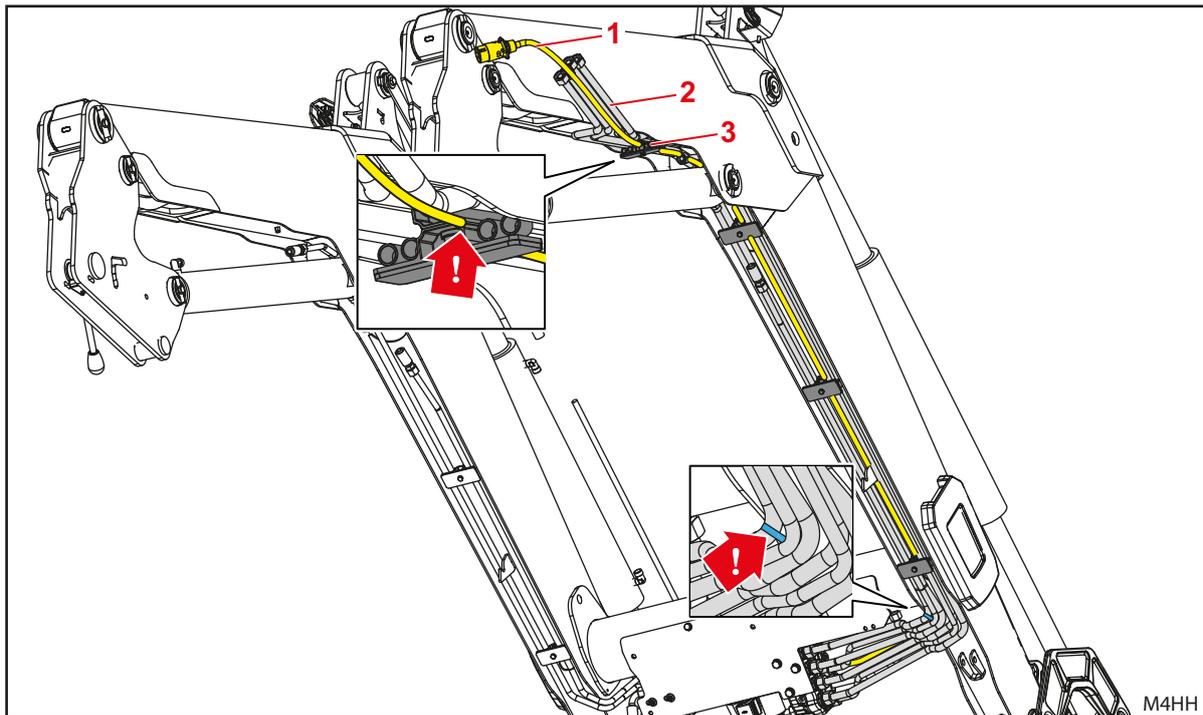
Panoramica – Posa del cavo del caricatore frontale
